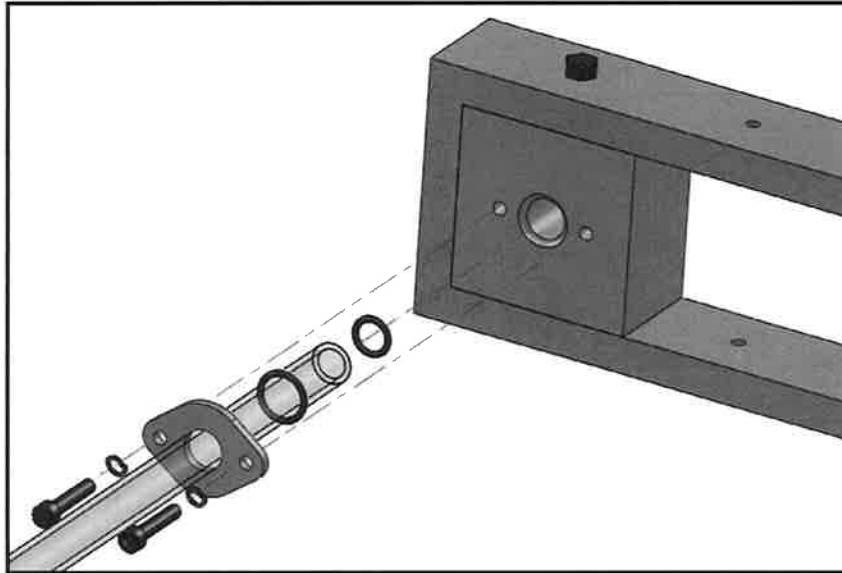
Ensamble de O-rings y placa para sujeción de tubos de cuarzo.
